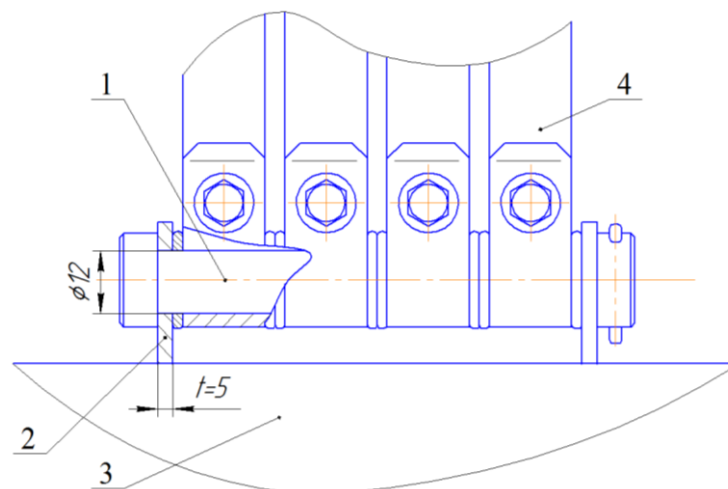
Розрахункова схема: 1 – вісь; 2 – вухо; 3 – труба; 4 – била.
